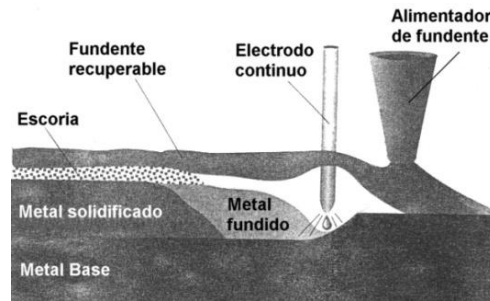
Proceso de soldadura de arco sumergido
